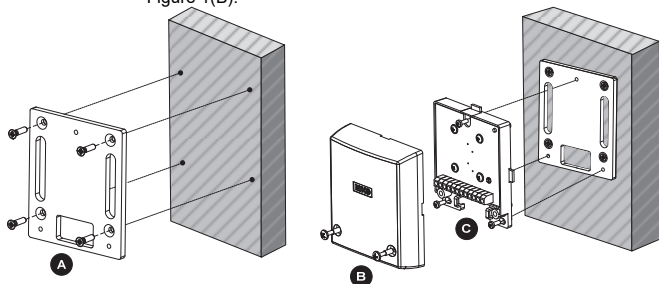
Montage du détecteur à l'aide de la plaque de montage. (Remarque: Fixer la plaque de montage au moyen de vis de fixation ou éventuellement, par soudage de la plaque sur une surface métallique.)
